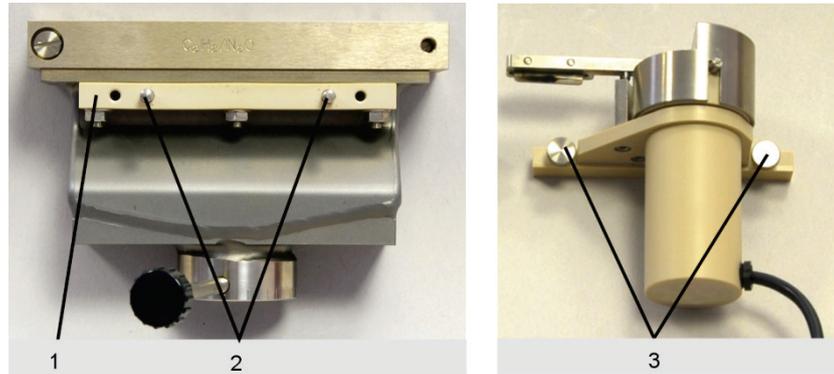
Befestigungsschiene am Brenner/Rändelschrauben am Scraper
